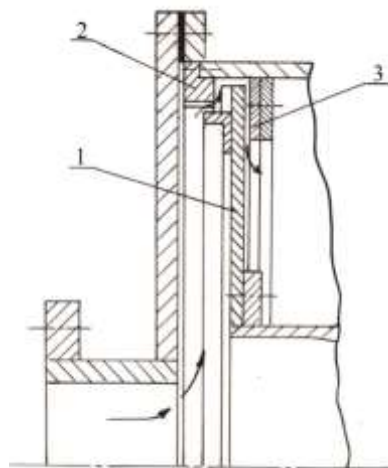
Гидродинамическое уплотнение для испытания на лабораторном стенде
